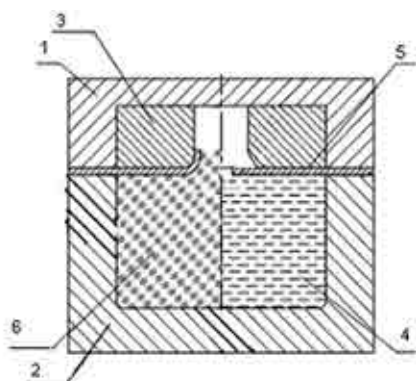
Устройство для отбортовки отверстий в листовой заготовке
